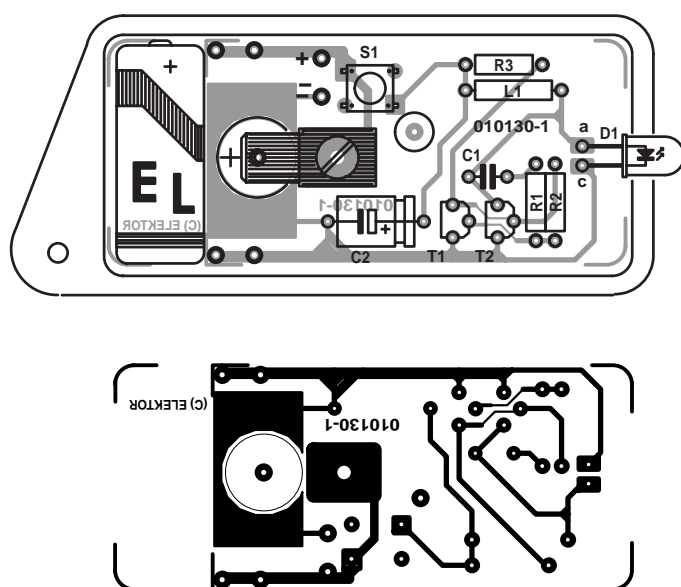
La platine laisse suffisamment de place pour une alimentation soit par « grosse » pile R1 soit par pile-bouton.
